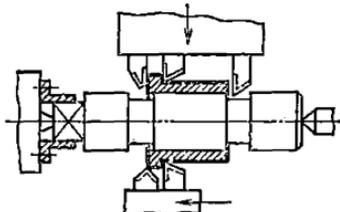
Наладка токарного многолезцового полуавтомата для обтачивания наружной поверхности и подрезания торцов.
